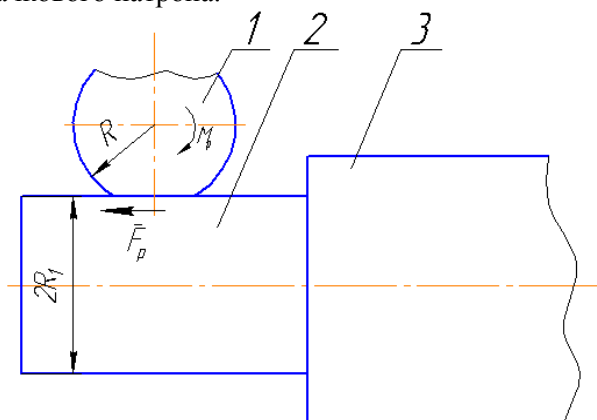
Вид сверху: 1 – фреза, 2 – заготовка, 3 – патрон
